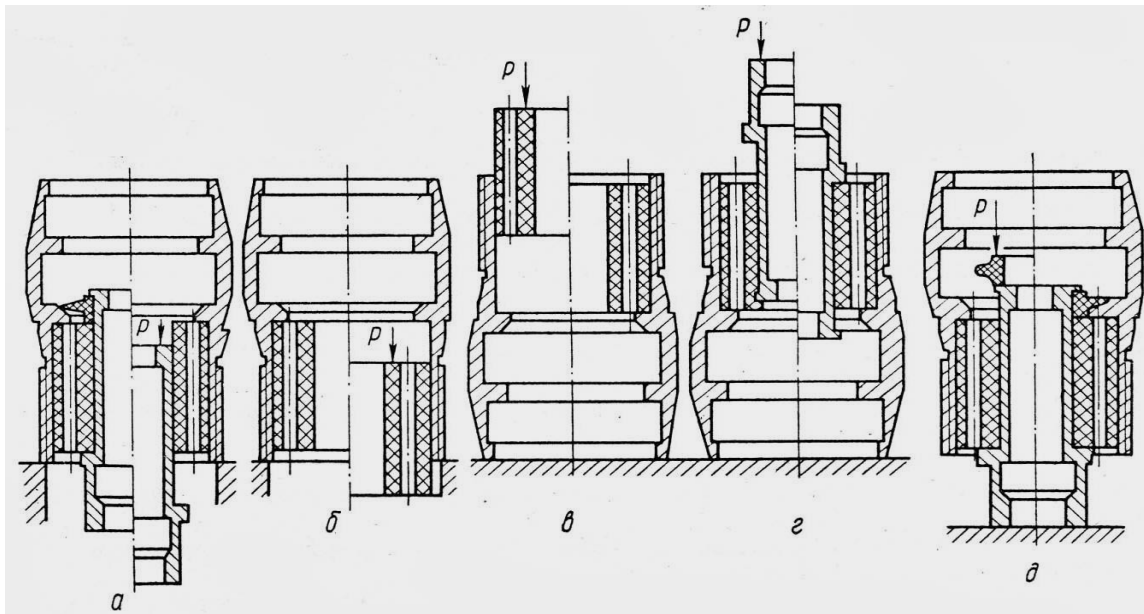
Схема выпрессовки – запрессовки деталей золотника
